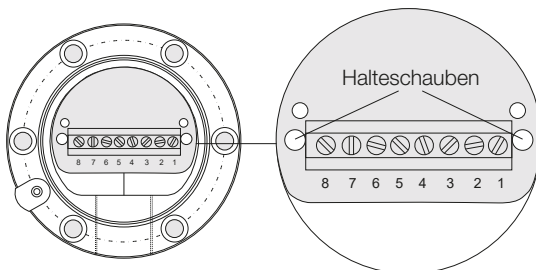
Typisches Gehäuse mit Anschlussklemmenbaugruppe, Pinbelegung
